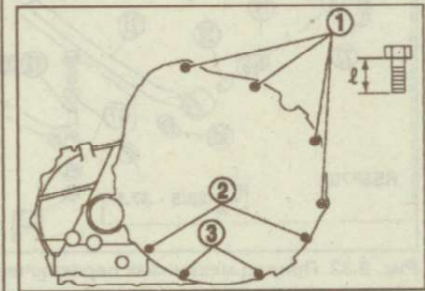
Расположение болтов крепления коробки передач RS5F50A
